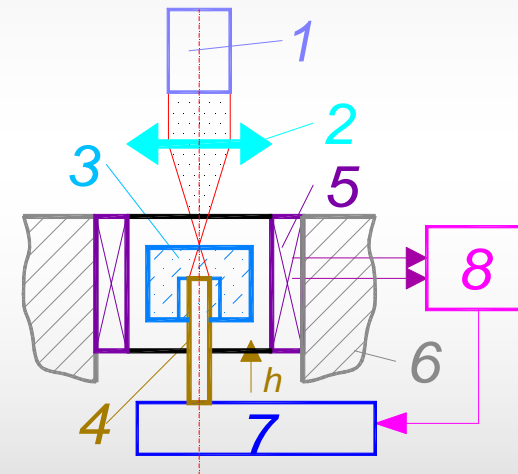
(19.1).ЛТУ для обробки отворів циліндричної форми
